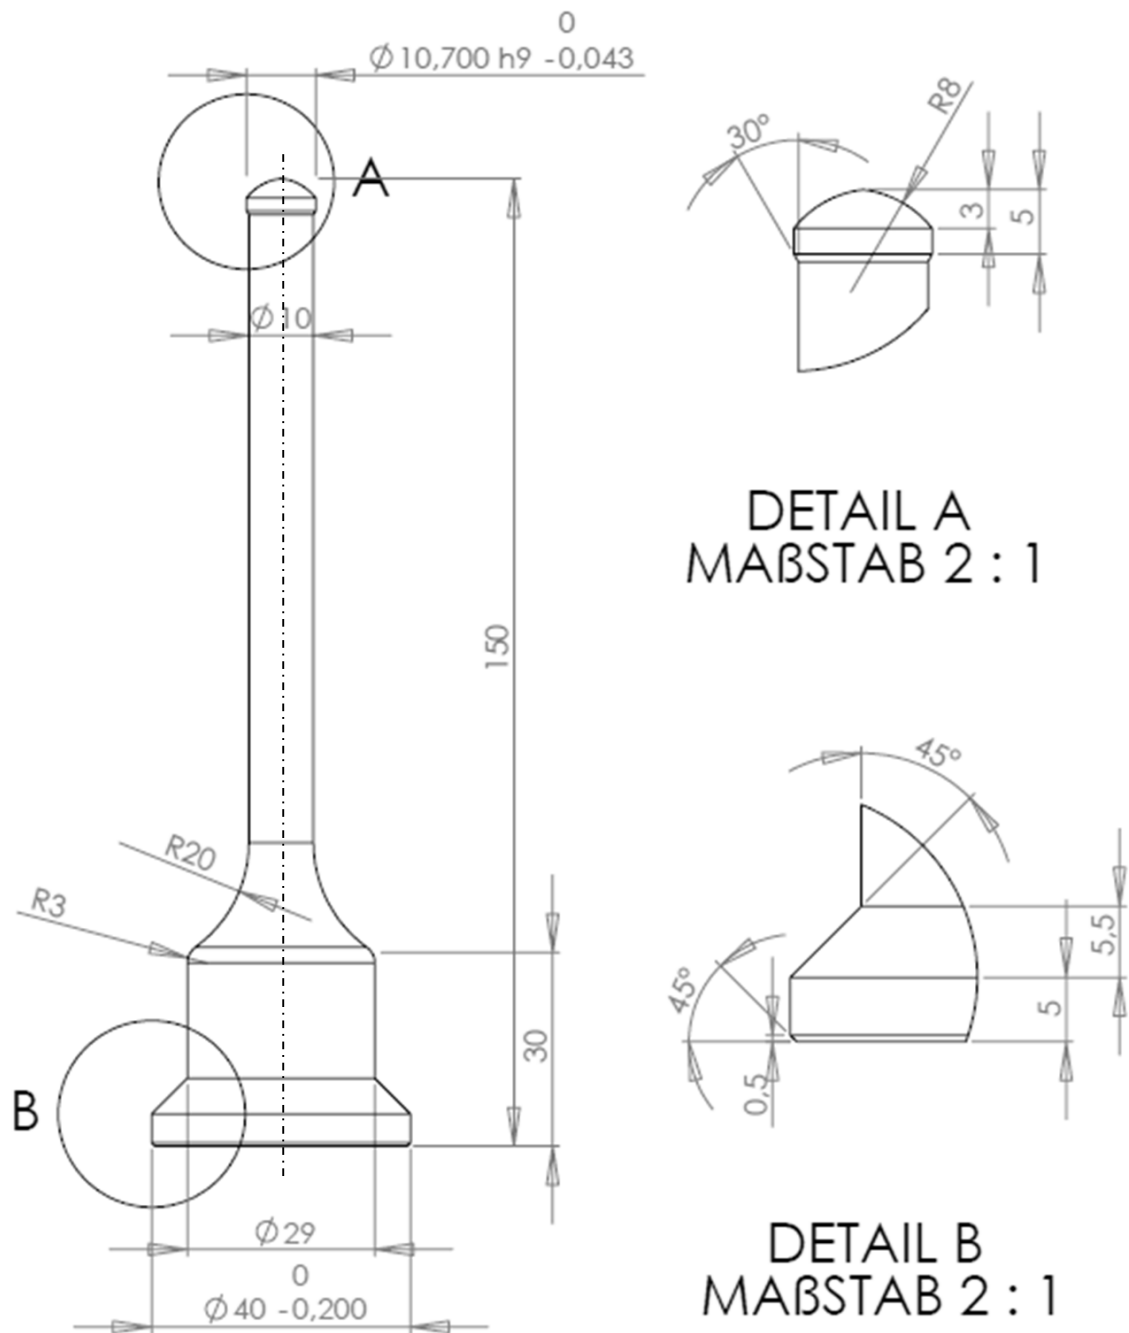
Technische Zeichnung des Gegenstempels für das Fließpressen.
